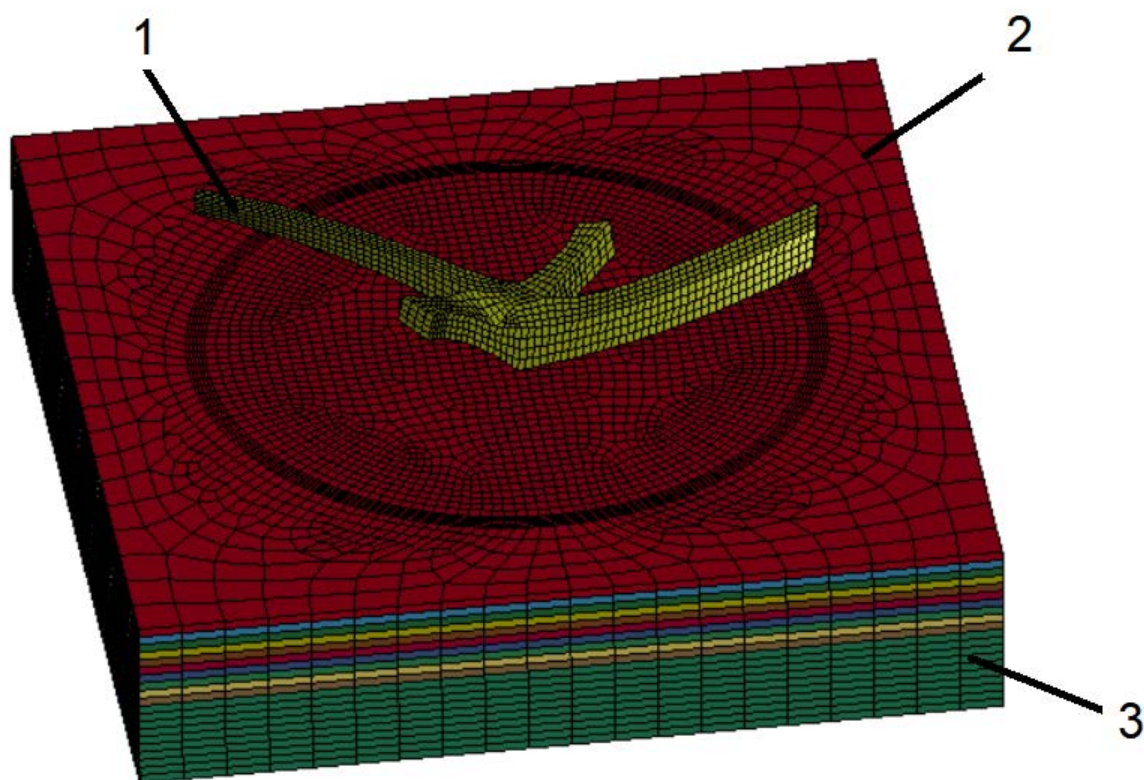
Модель сверла и пакета для моделирования процесса сверления: 1 – сверло; 2 – слой композита; 3 – слой металла
